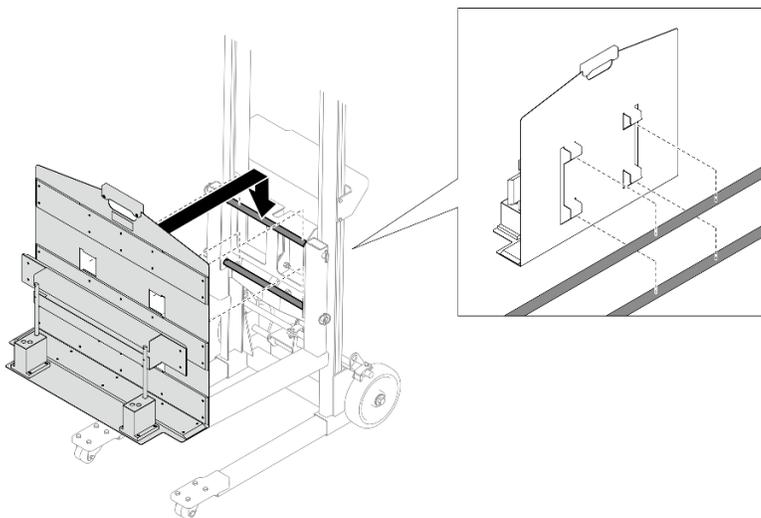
Fixation du dispositif d'outil de levage sur l'outil de levage
